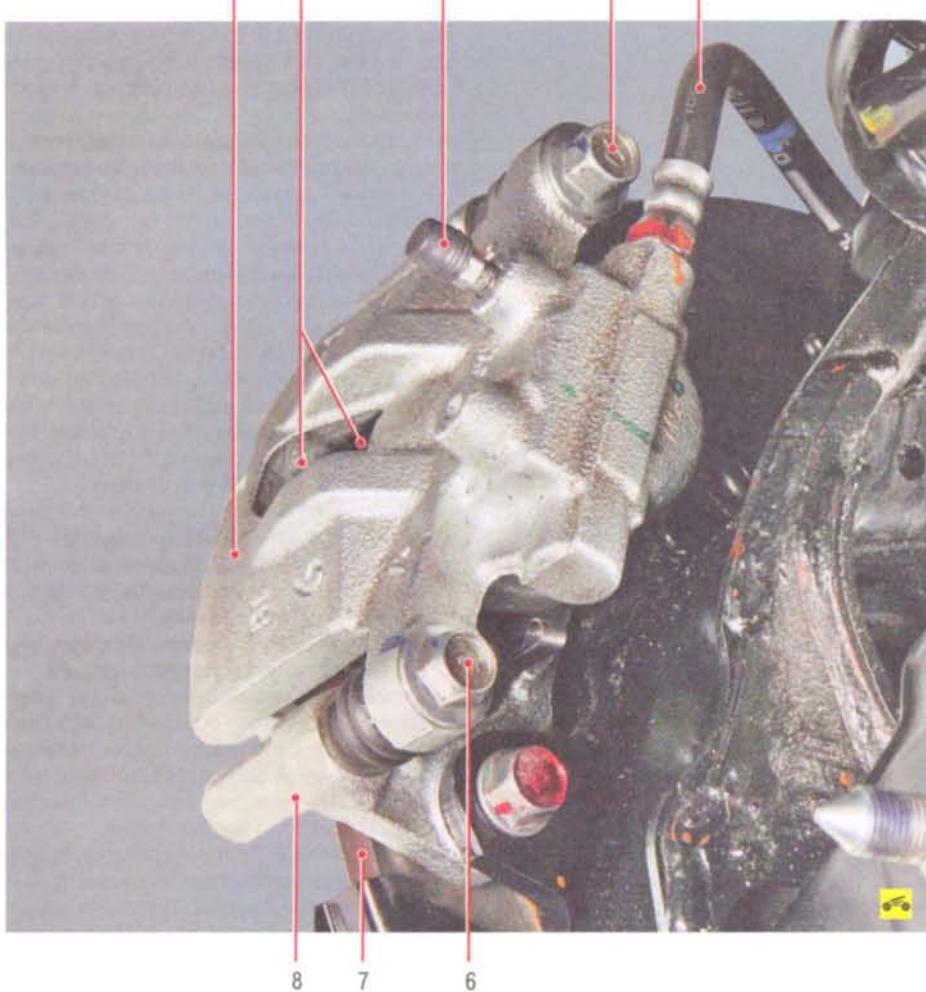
Детали заднего рабочего тормозного механизма: 1 – суппорт; 2 – тормозные колодки; 3 – клапан выпуска воздуха; 4 – верхний направляющий палец суппорта; 5 – тормозной шланг; 6 – нижний направляющий палец суппорта; 7 – тормозной диск; 8 – направляющая тормозных колодок
